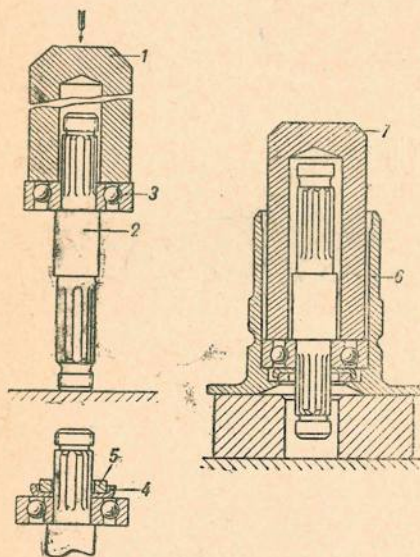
Сборка стакана вертикального валика переключения коробки перемены передач
